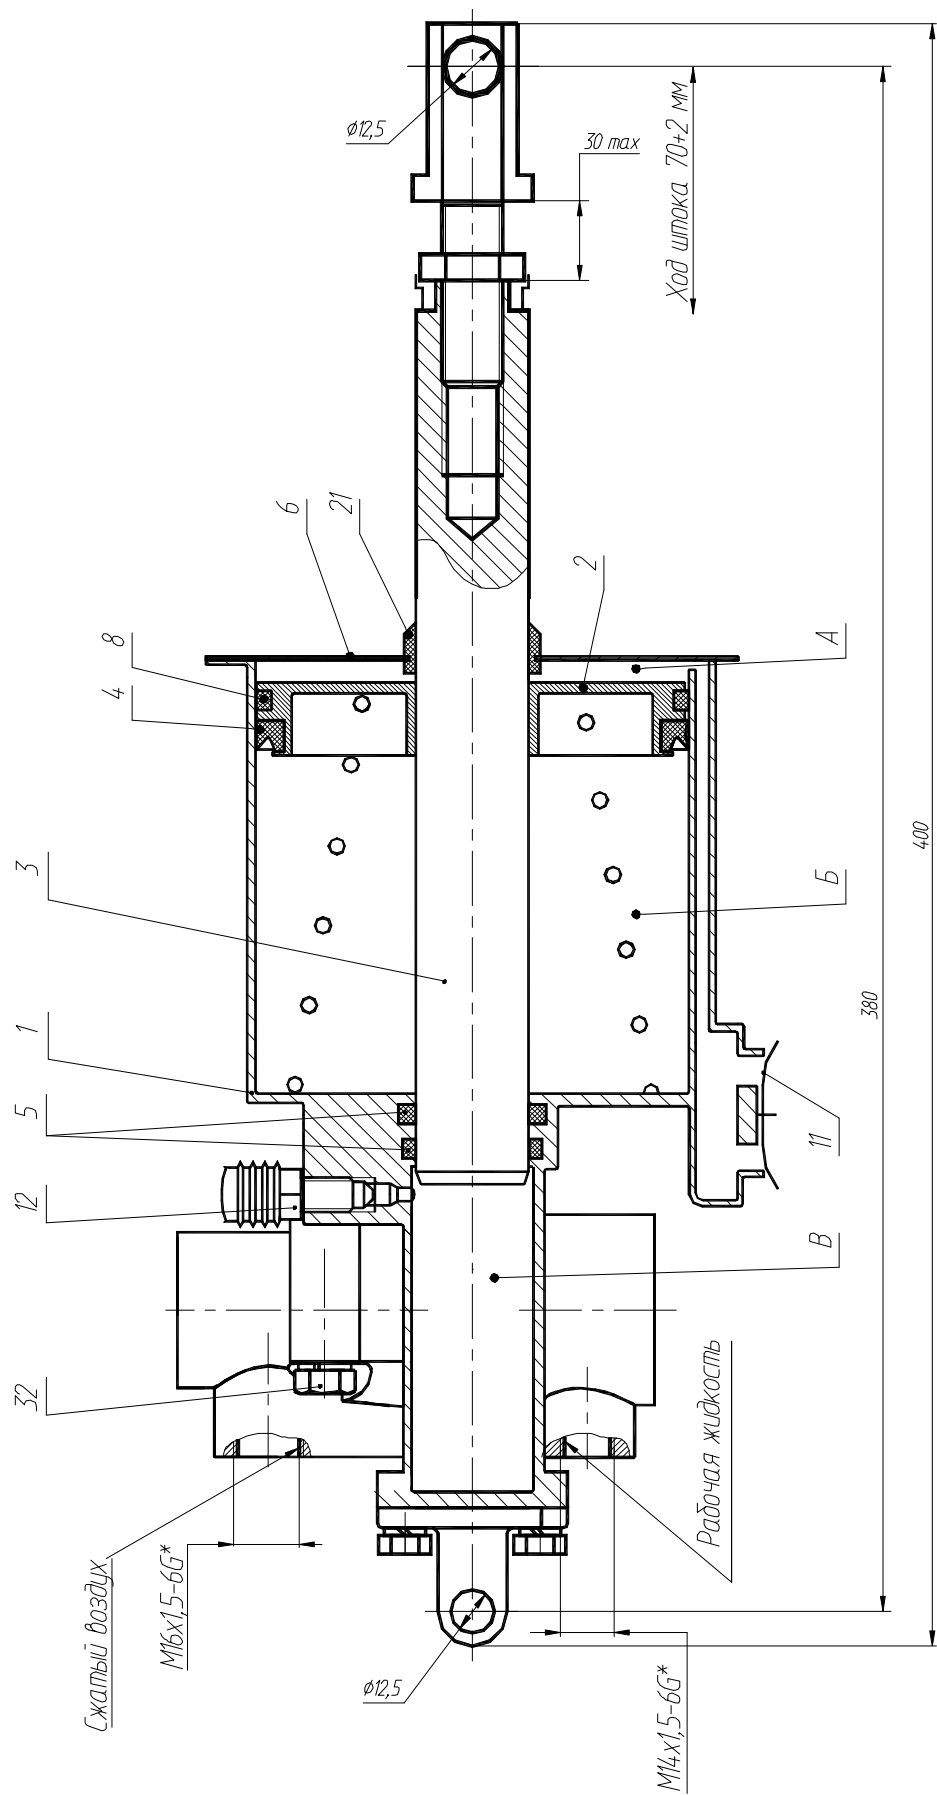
Схема пневмогидравлического усилителя привода сцепления
